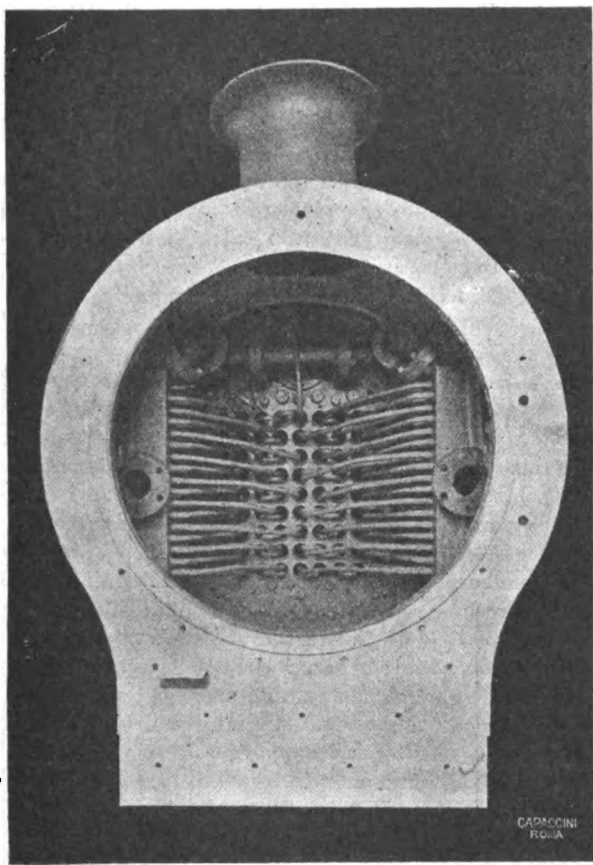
Vista del surriscaldatore Robinson per locomotive
